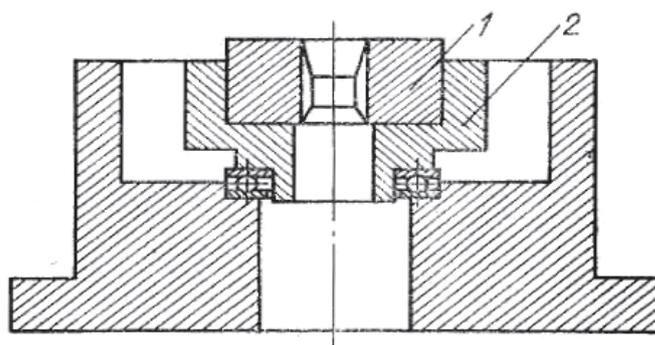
Штамп для получения профиля зубьев с чистовыми размерами
